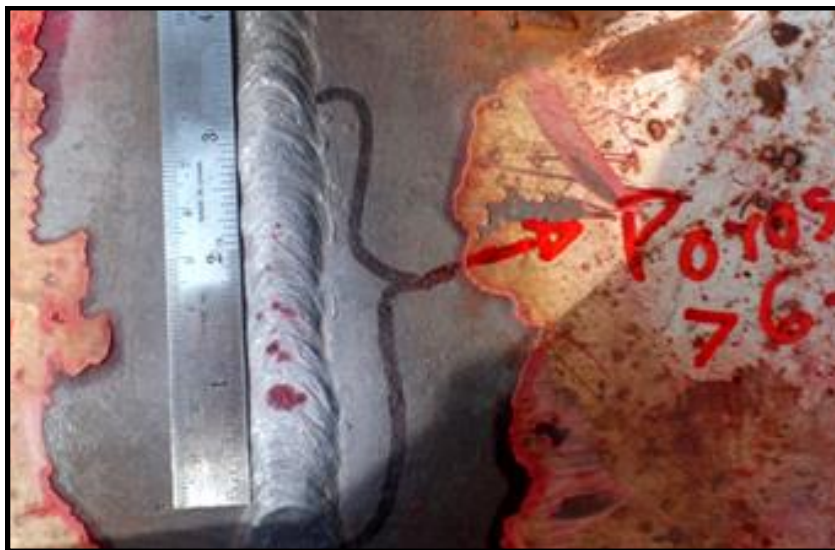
Porosidad aislada en una soldadura (2, 94)
